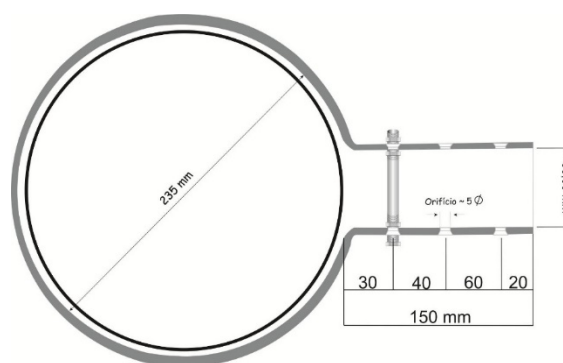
Abraçadeira para fixação do modelo de pluviômetro ANA.
